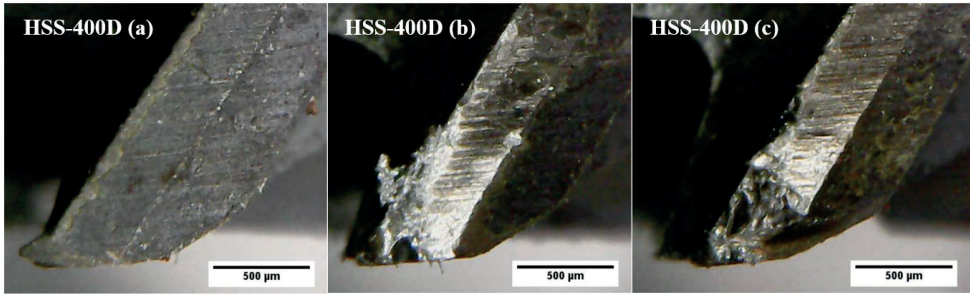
Fresa HSS-400D. a) antes do ensaio b) camada TiN removida c) fratura acentuada
